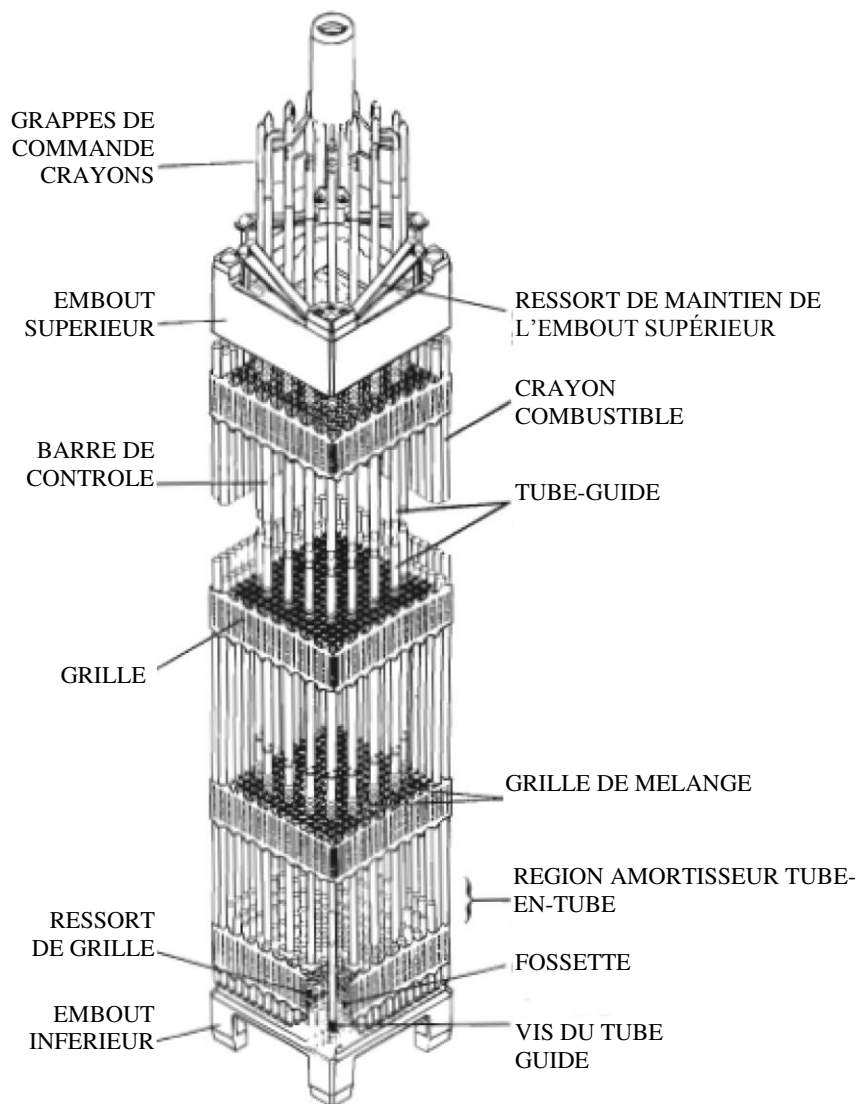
Section d'assemblage combustible 17x17 Optimisé avec RCC
